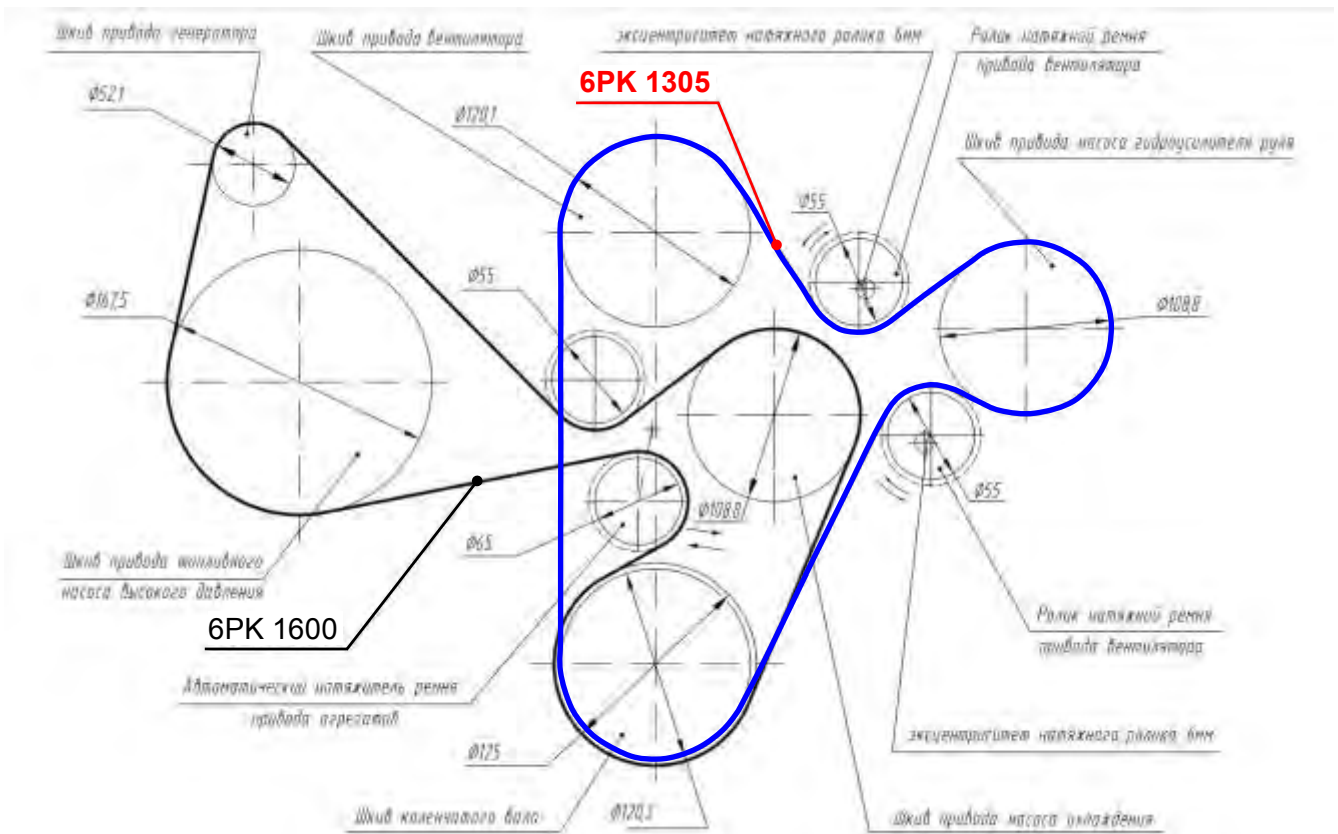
Схема привода вспомогательных агрегатов двигателя для автомобилей на платформе УАЗ-315148.
